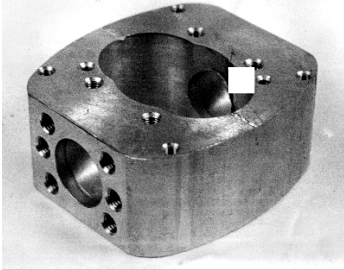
Корпус водяного лічильника з різьбовими отворами
